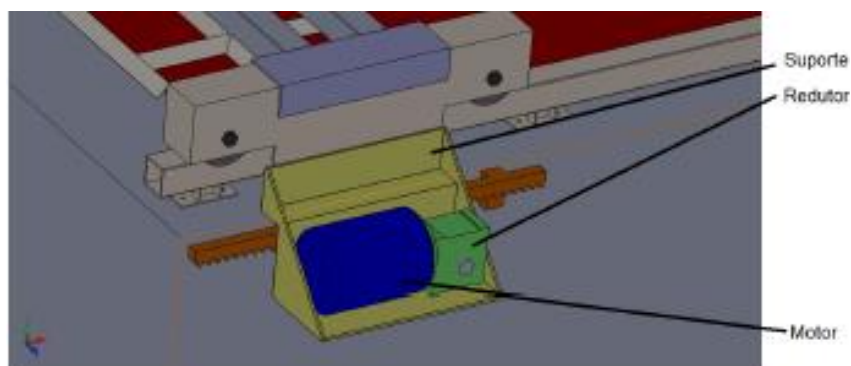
Estrutura que irá suporta o motor com a caixa redutora fixa à estrutura.
